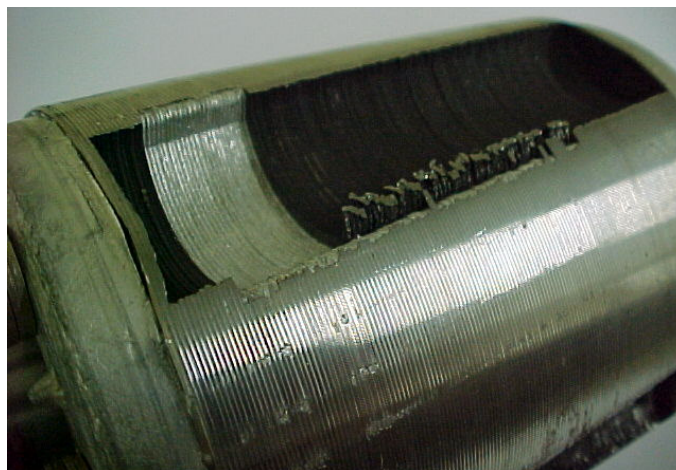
Rotor do projeto 4 – falhas na usinagem
